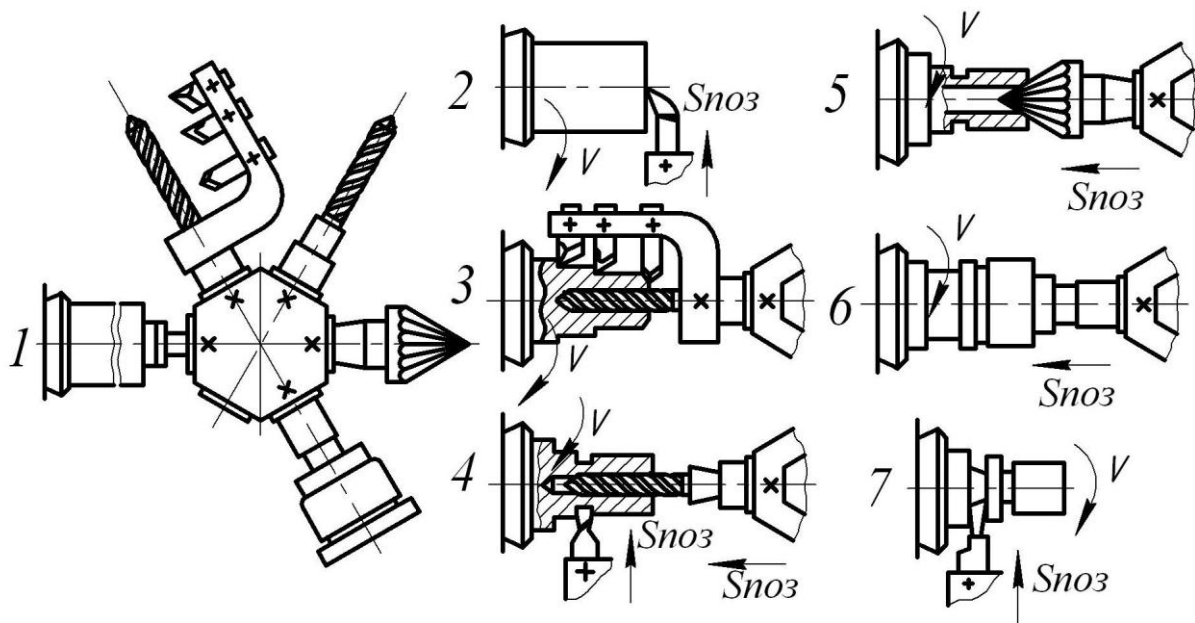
Схеми обробки поверхонь заготовки на револьверному верстаті:
